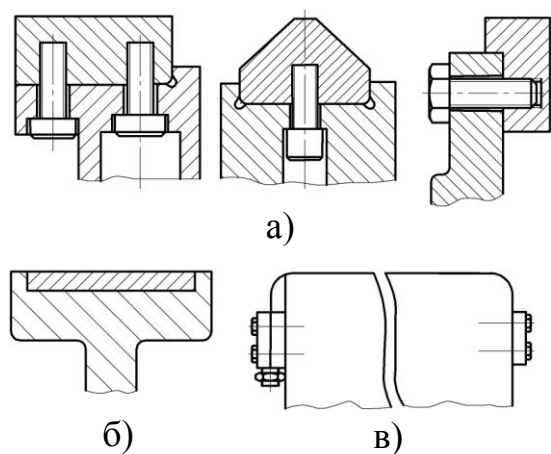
Накладні напрямні ковзання: а – накладні планки; б – загартовані пластини; в – сталеві стрічки
